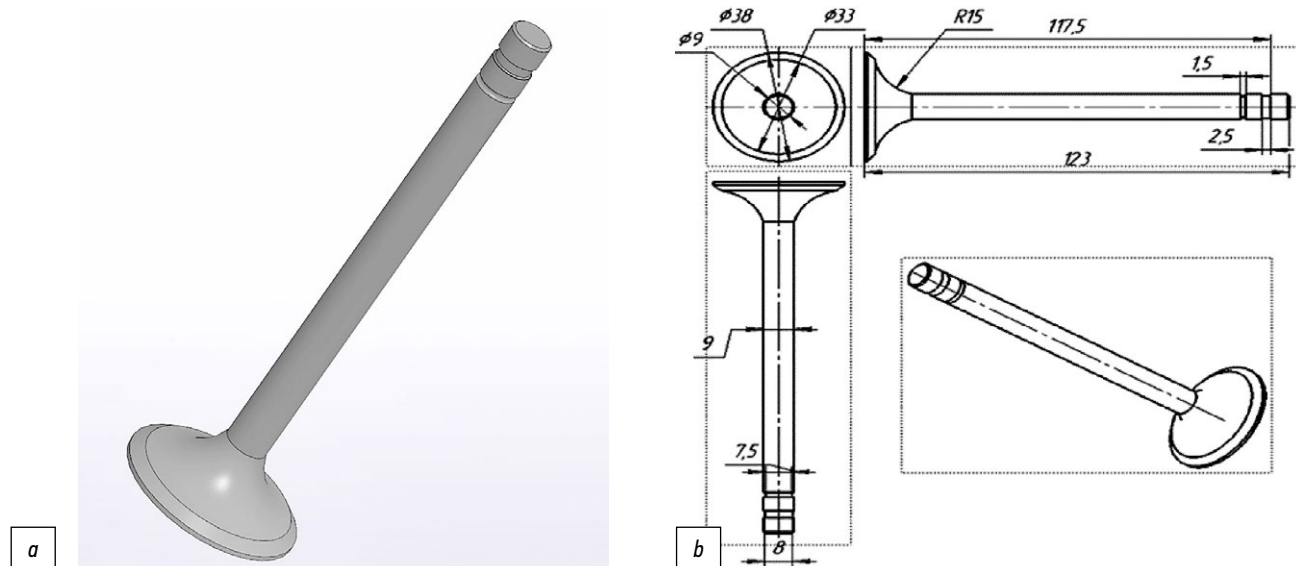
Общий вид исследуемого клапана судового малоразмерного двигателя Ч8,5/11: *a* — представленный в 3D модели; *b* — основные размеры клапана [8].
